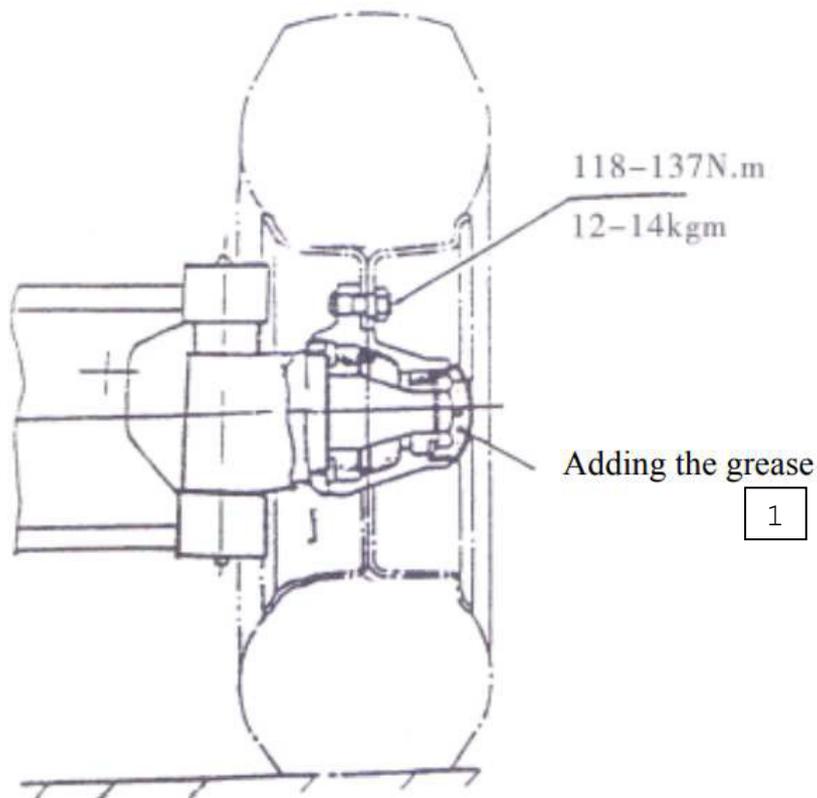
Добавление консистентной смазки и регулировка предварительного натяжения:
